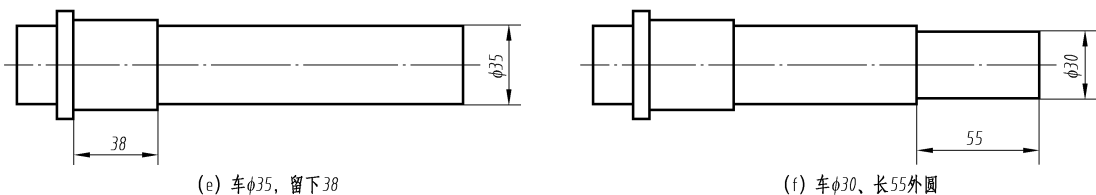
输出轴车削加工顺序和尺寸标注 (续)
